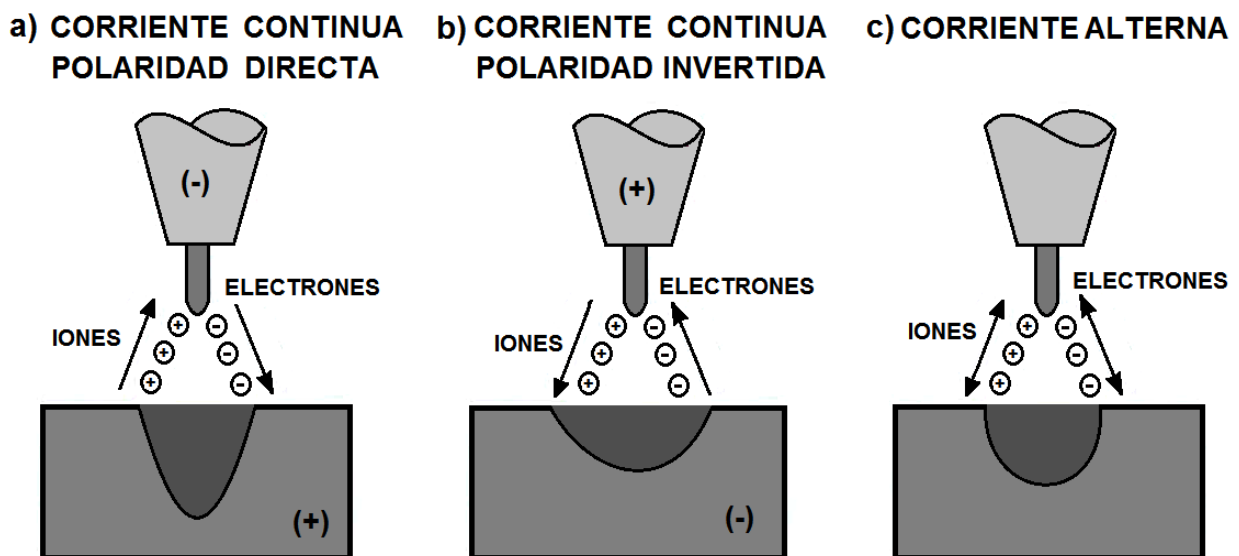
Esquema de la polaridad y la penetración en el proceso de soldadura GTAW
